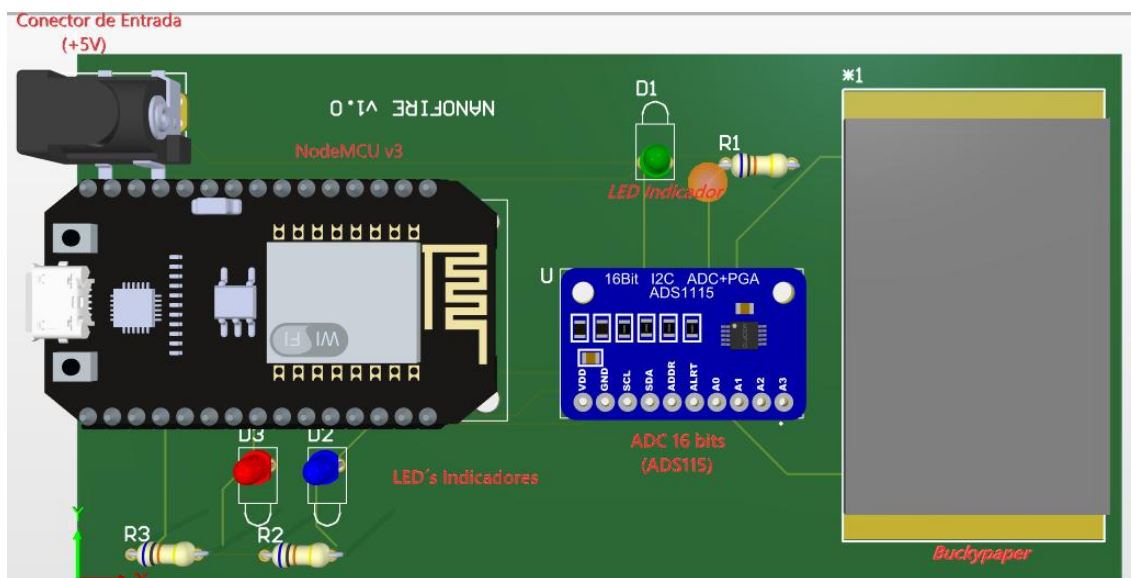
Projeto de PCB, para integração IoT do BP.
